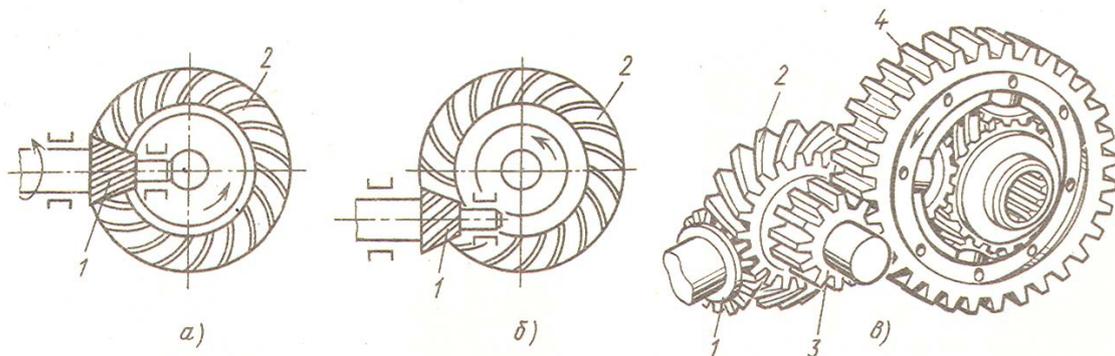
Главные передачи: а – коническая; б – гипондная; в – двойная; 1 и 2 – ведущее и ведомое конические зубчатые колеса; 3 и 4 – ведущее и ведомое цилиндрические зубчатые колеса
